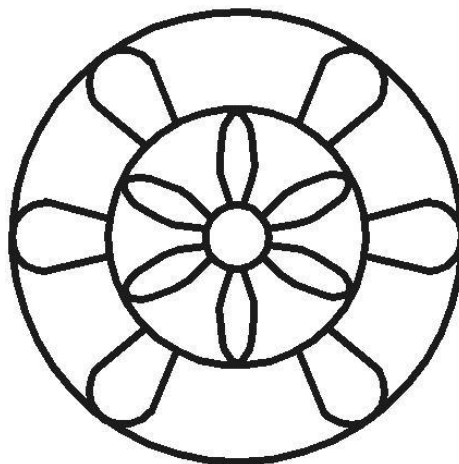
Конструкція робочого колеса вентилятора з лопатками
